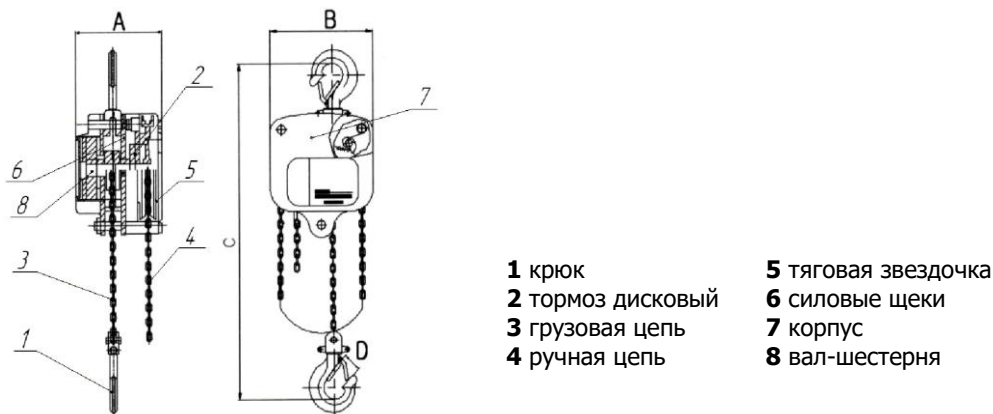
Устройство тали ручной шестеренной 622-А.
